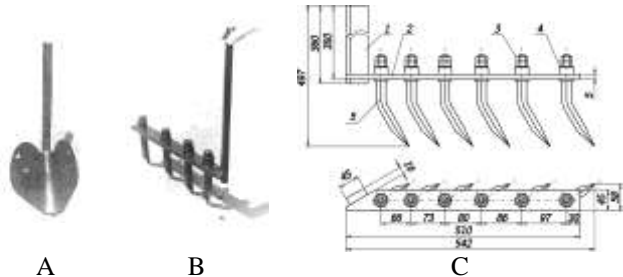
Розроблені робочі органи: А — борозноріз; В і С — загортач (зовнішній вигляд і креслення)
